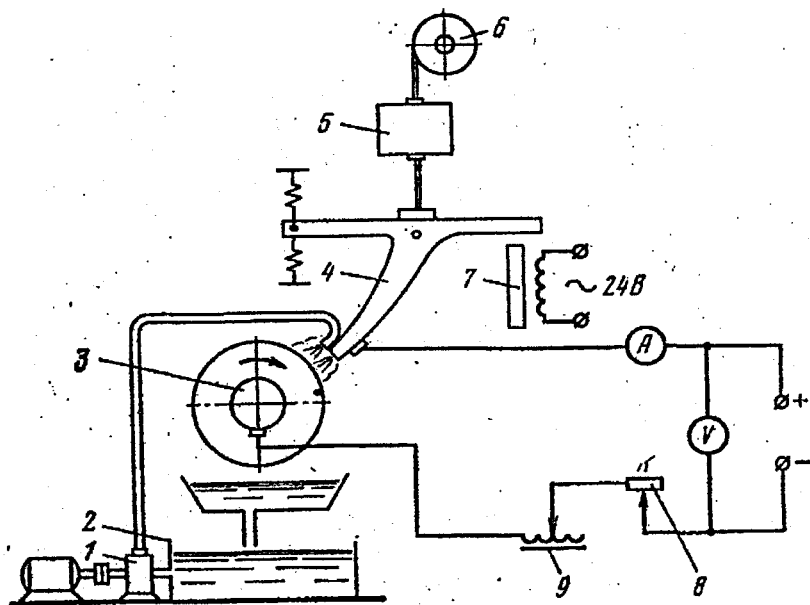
Схема установки для вібродугового наплавлення: 1 – насос, 2 – бак, 3 – наплавлювана деталь, 4 – мундштук, 5 – механізм подачі дроту, 6 – касета, 7 – електромагнітний вібратор, 8 – реостат, 9 – індуктивний опір
